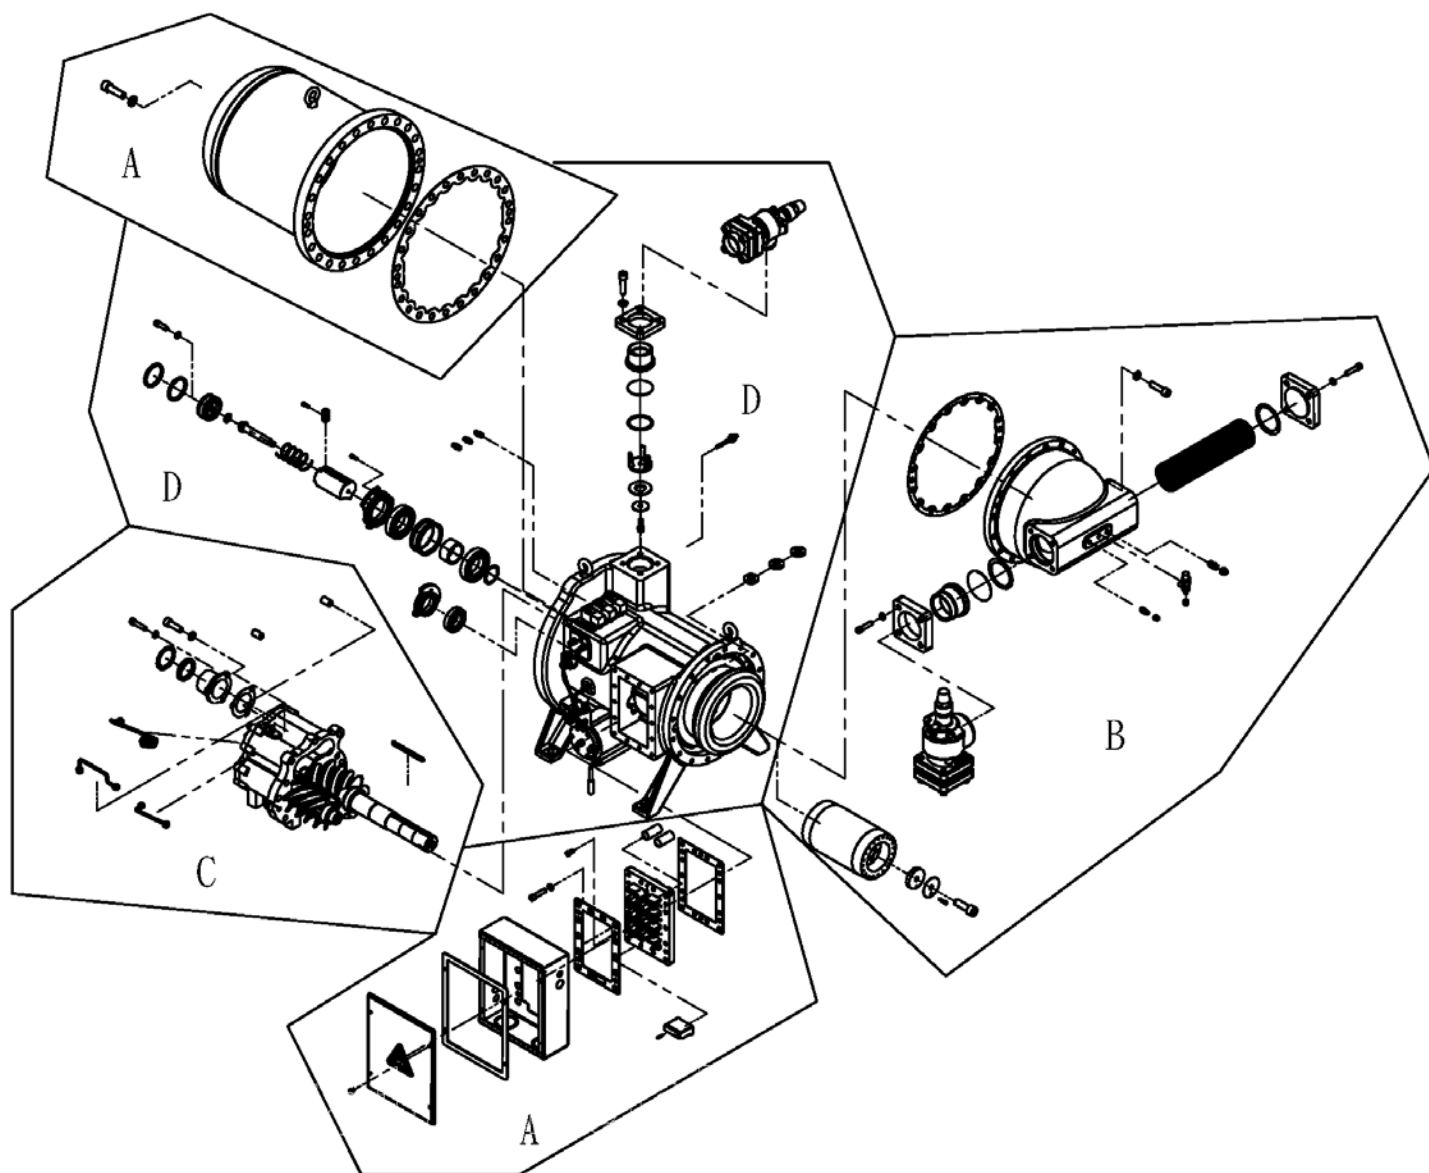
SR-434 (H)II 分解說明/ Disassembly illustration
